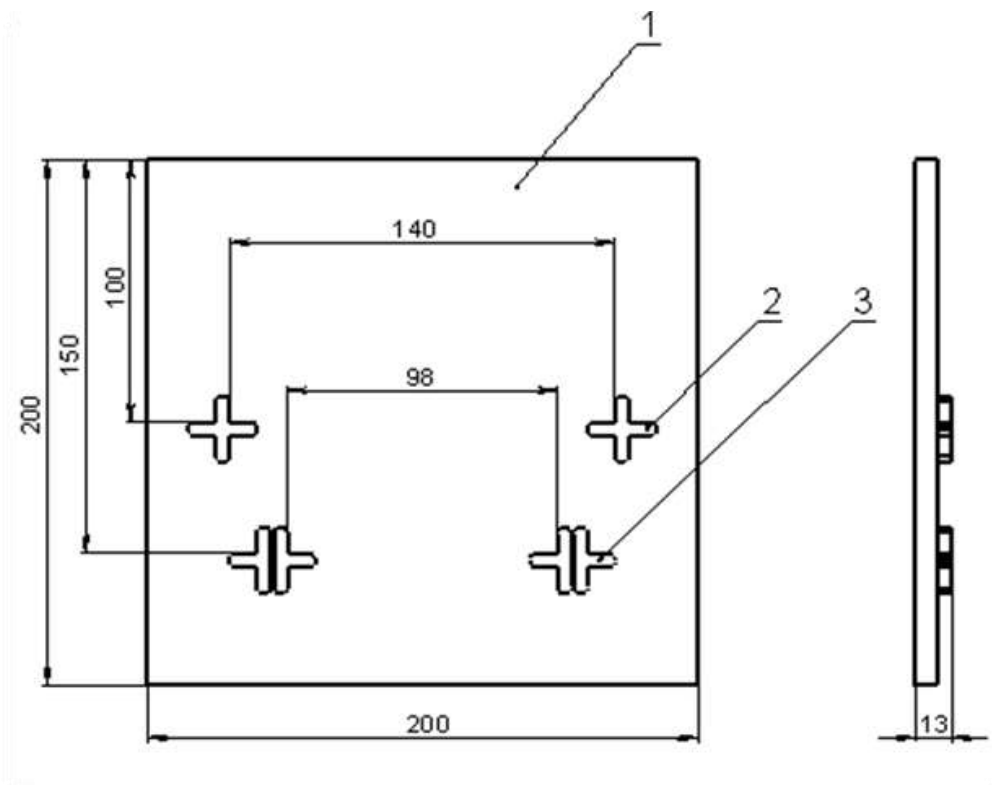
Пластина для припаювання тонкої шини (фольги)
